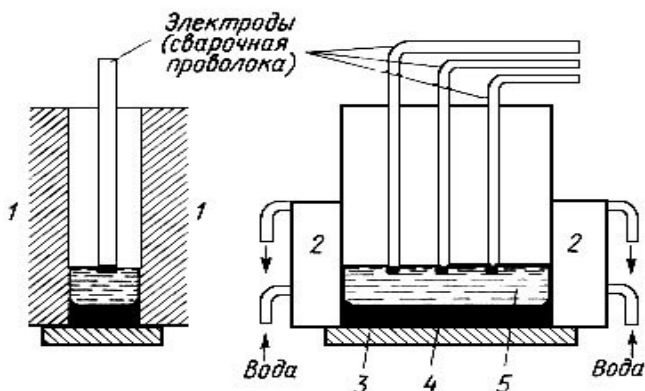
Схема процесса электрошлаковой сварки: 1 – свариваемые кромки изделия; 2 – медные ползуны; 3 – начальные планки; 4 – расплавленный металл; 5 – жидкий шлак
